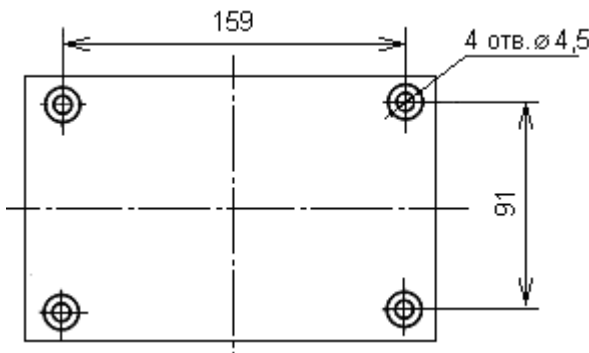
Крепление адресного блока (присоединительные размеры)
